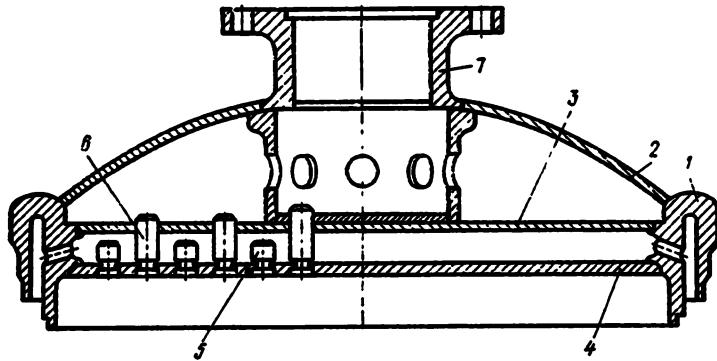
Конструкция форсуночной головки с плоским днищем:
